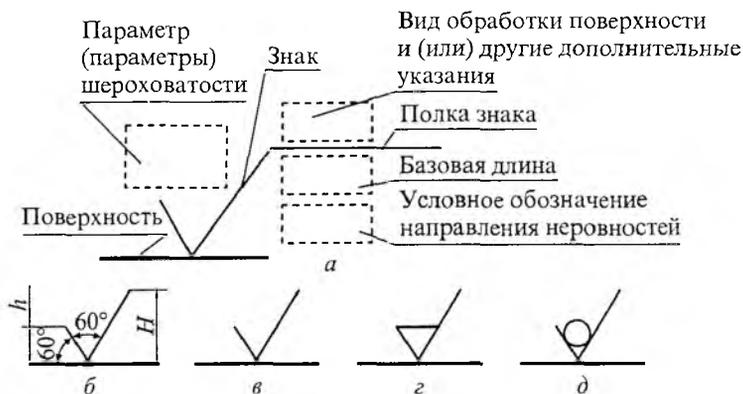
Структура и знаки обозначения шероховатости поверхности:
